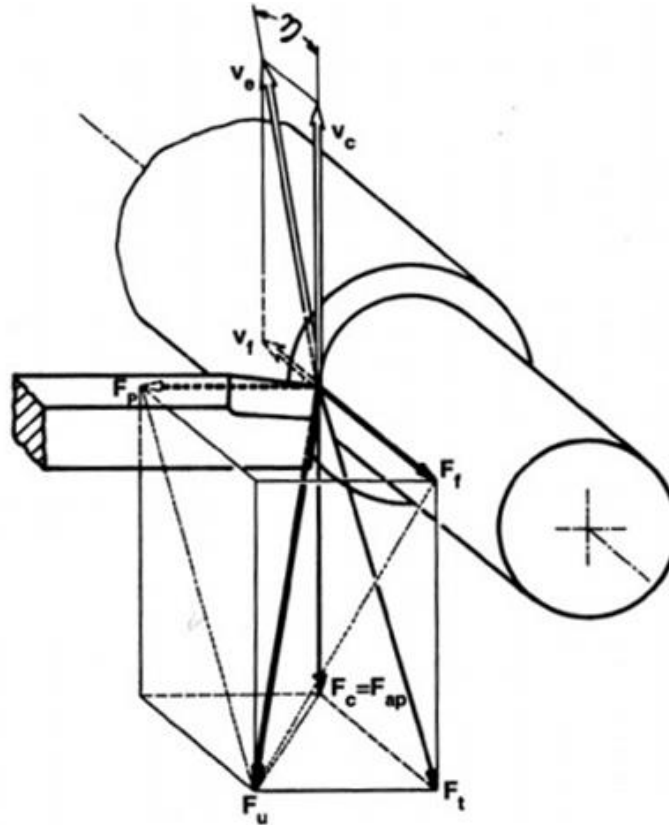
Componentes da força de usinagem no torneamento.
